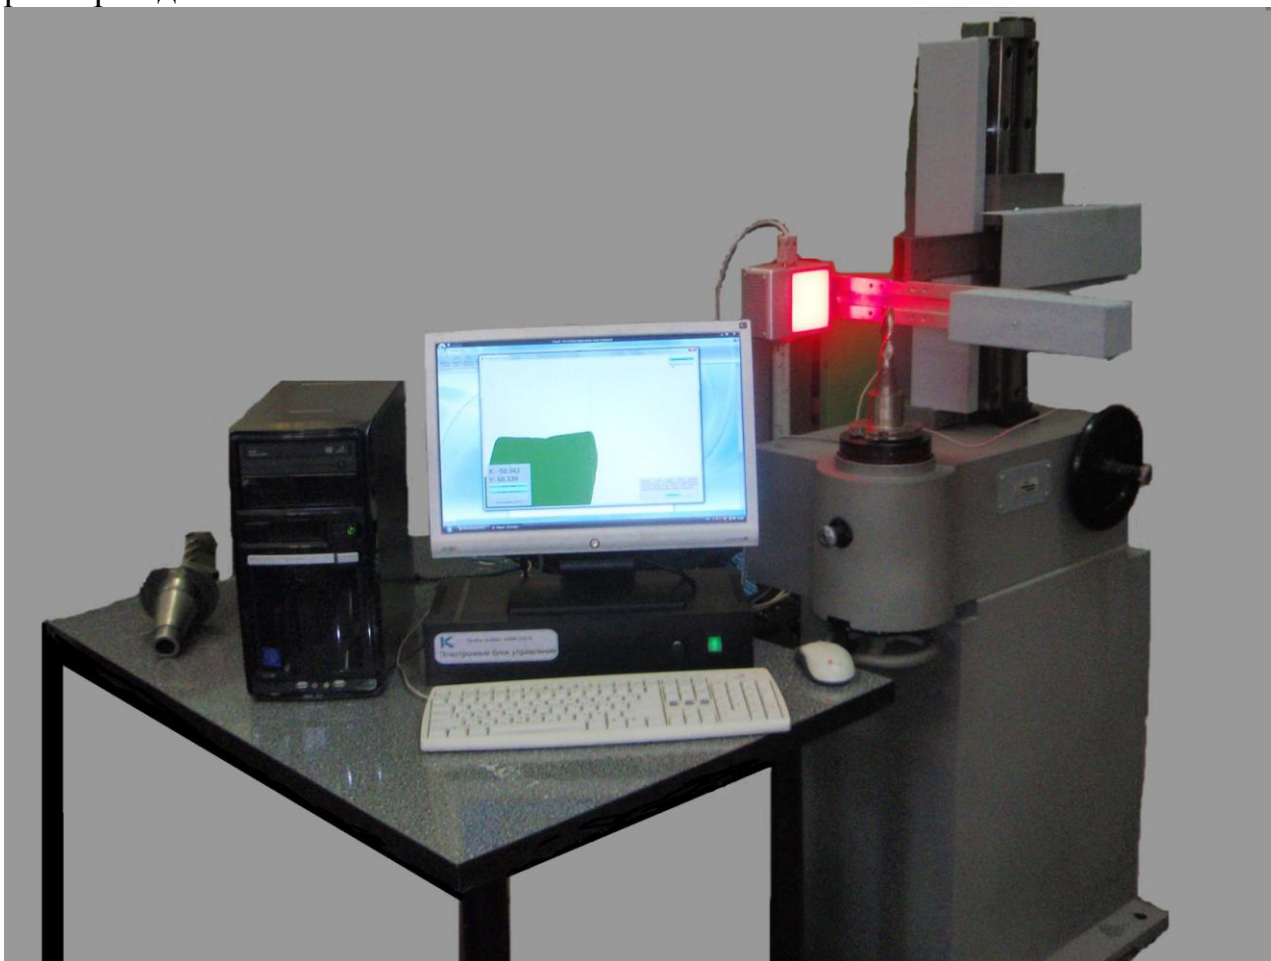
Прибор для размерной настройки ИК станков СФР группы НИИК-2027К
